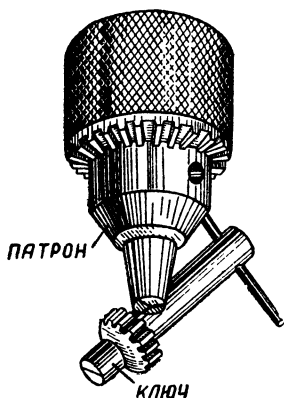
Сверлильный патрон трехкулачковый с наклонно расположенными кулачками.
